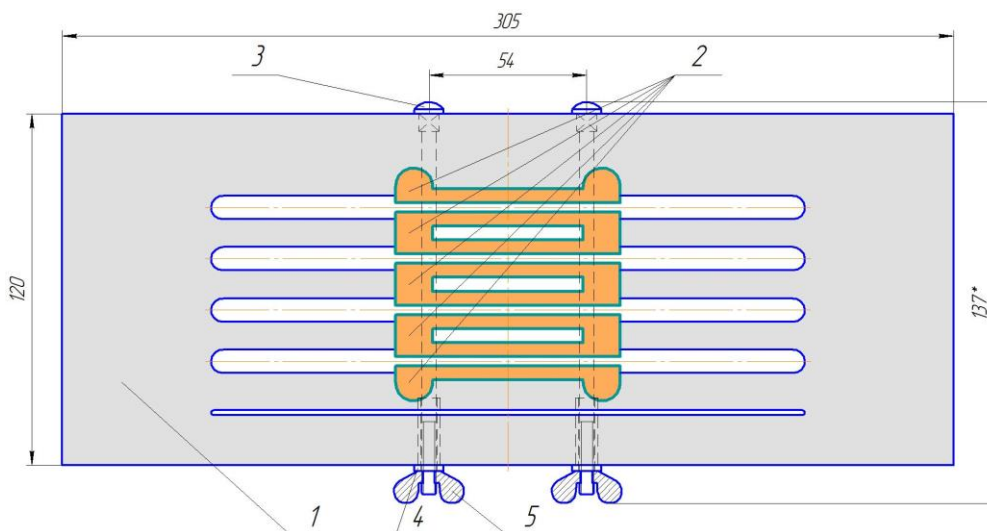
Зажимное приспособление (тиски) для медных пластин: 1 – корпус, 2 – губки медные, 3 – шпилька, 4 – втулка, 5 – гайка-барашек ГОСТ 3032.
